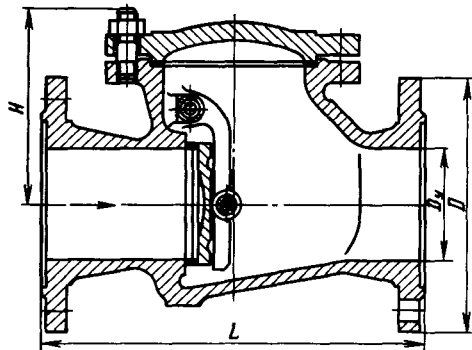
Клапан обратный поворотный типа 19с17иж
